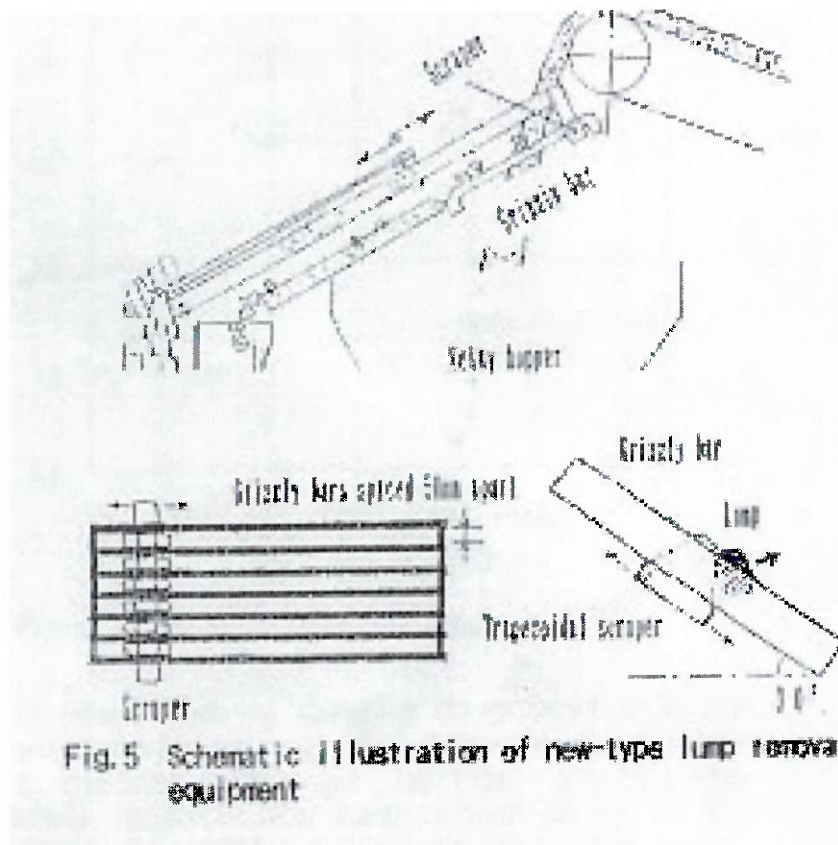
Ilustração esquemática do dispositivo de remoção de pedras⁽²⁾.
